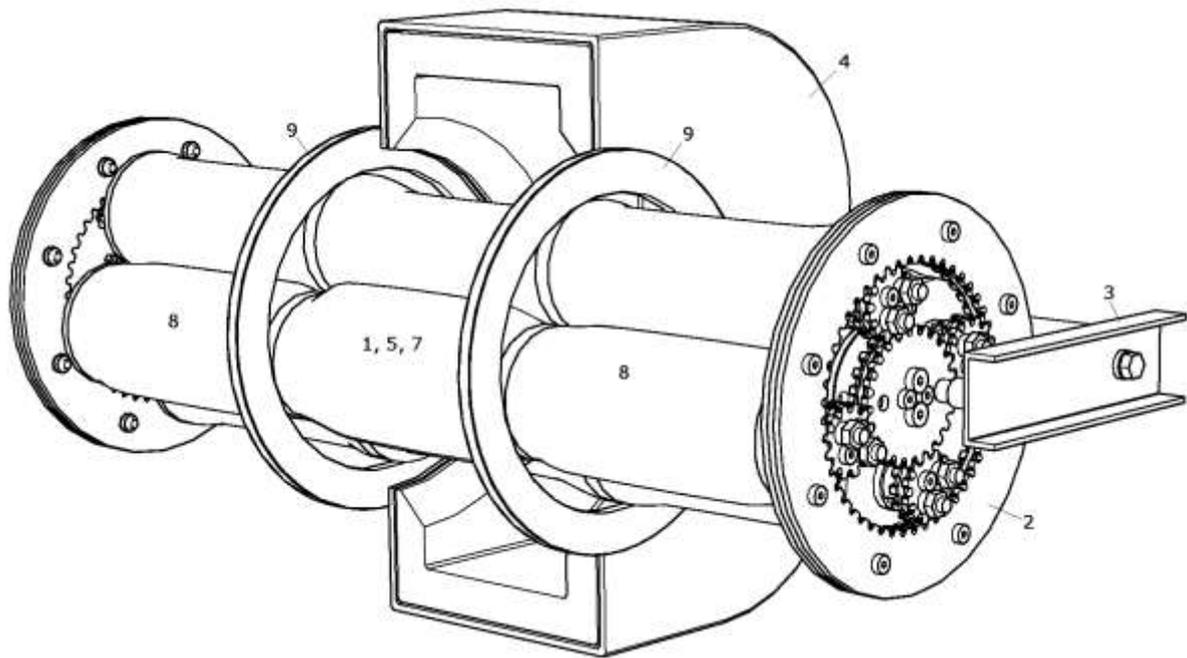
Geöffnetes Drehkolbenarray für einen Stirlingmotor, mit Totraumfüllern und Einspritzdüsen.
